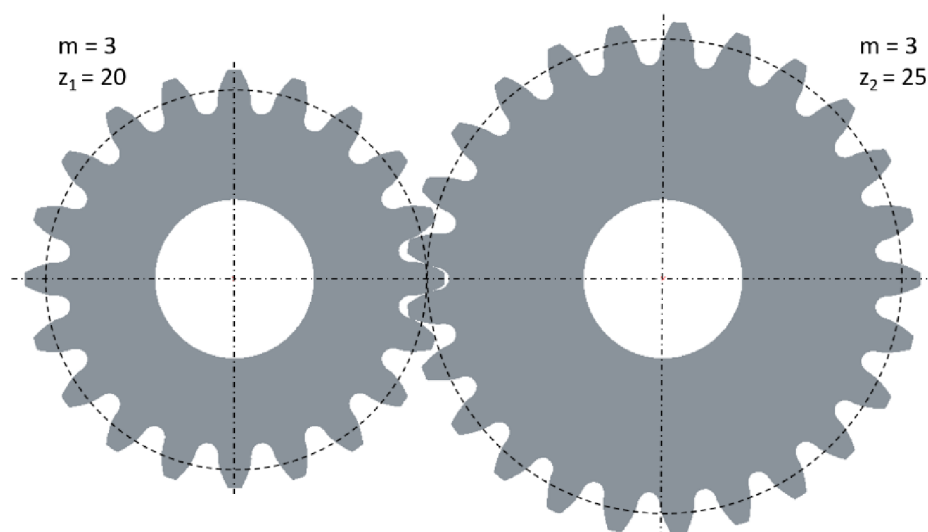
Finální tvar boku zubu a oblouk opisující roztečnou kružnici
